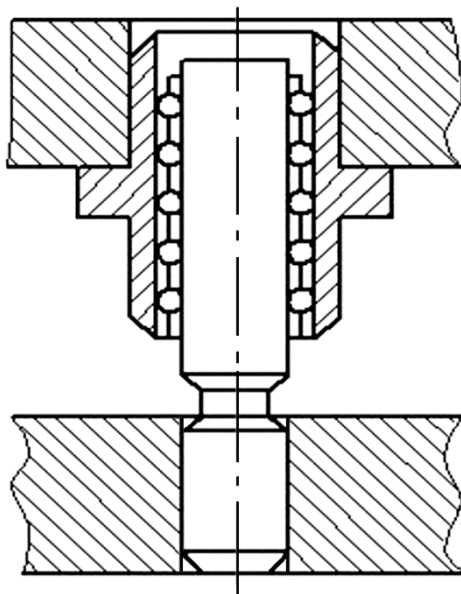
Загальний вигляд циліндричного напрямного вузла кочення
